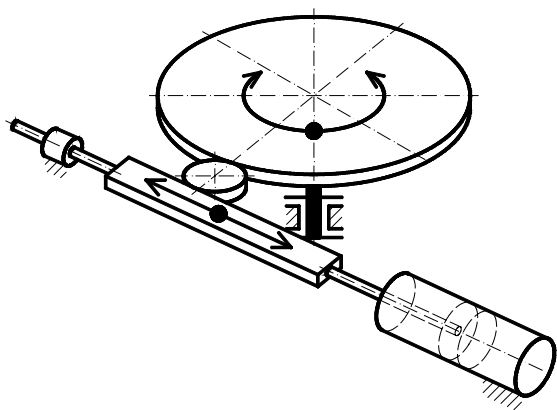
Rotační motor – kývavý pohyb
